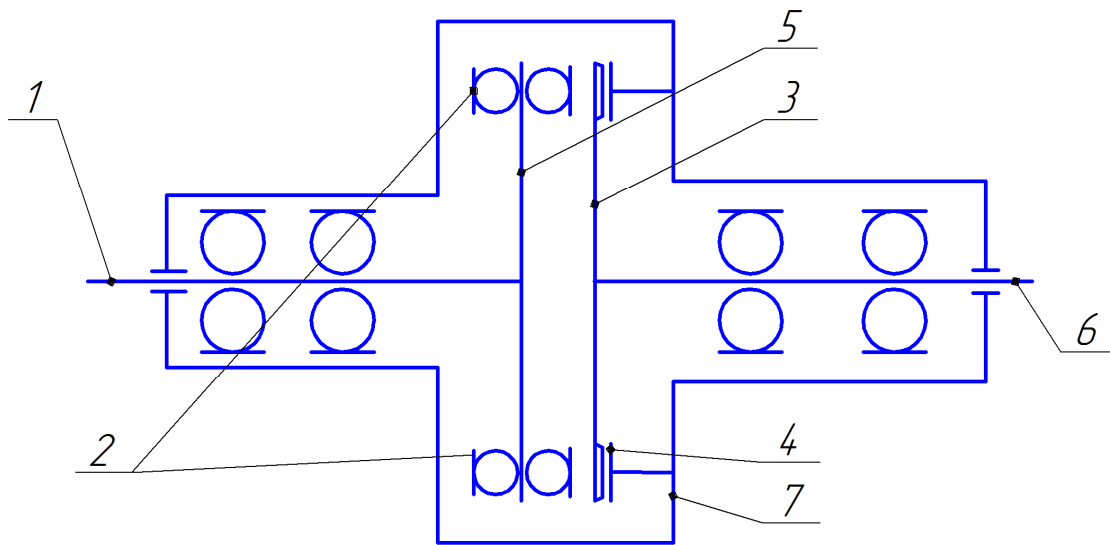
Кинематическая схема торцевой волновой зубчатой передачи: 1 - входной вал, 2 - подшипники генератора волн, 3 - гибкое колесо, 4 - жесткое колесо, 5 - корпус генератора волн, 6 - выходной вал
